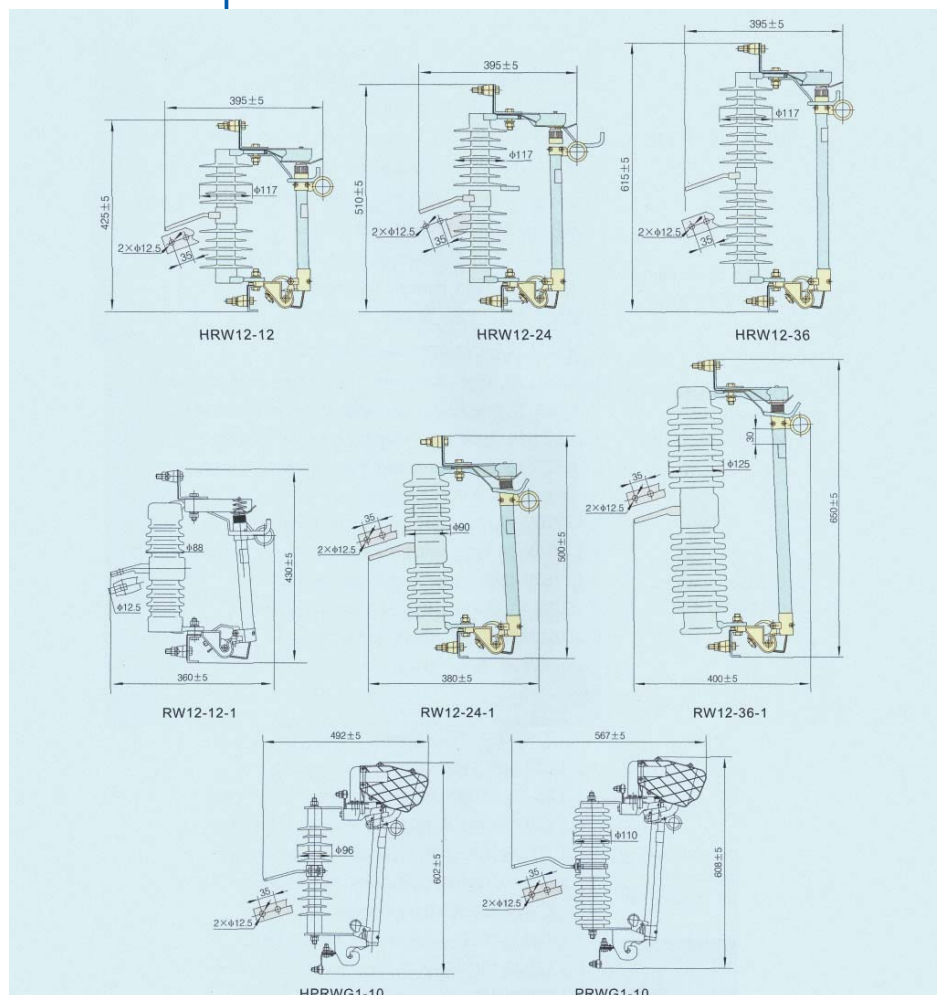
Внешний вид и размеры откидывающегося плавкого предохранителя
